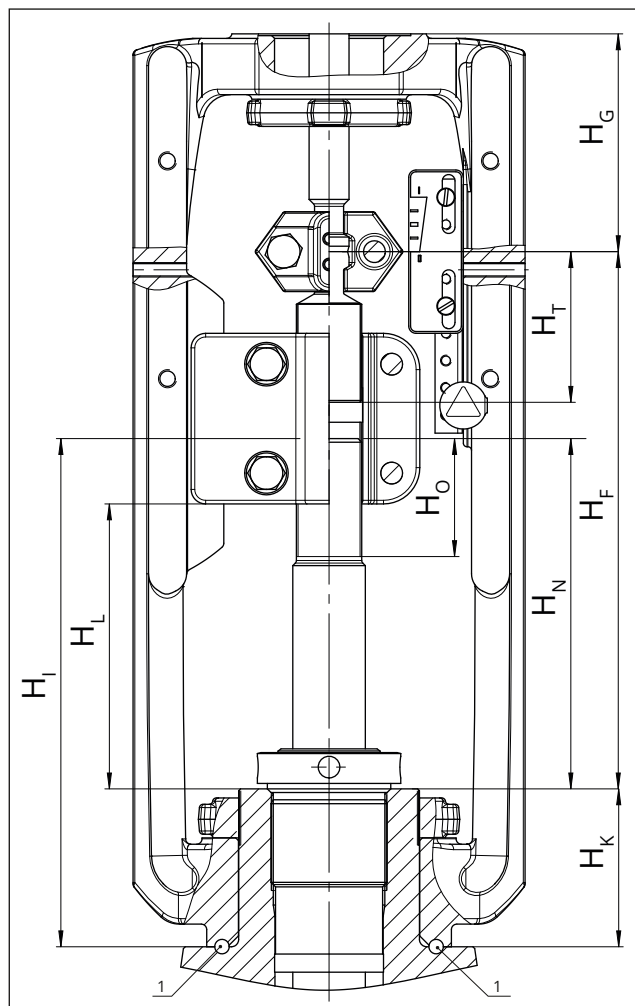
Чертеж с монтажными размерами для пневматических приводов Тип 3271 и Тип 3277
